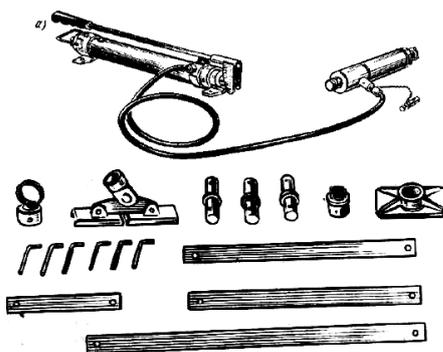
Гидравлическое устройство и набор приспособлений
